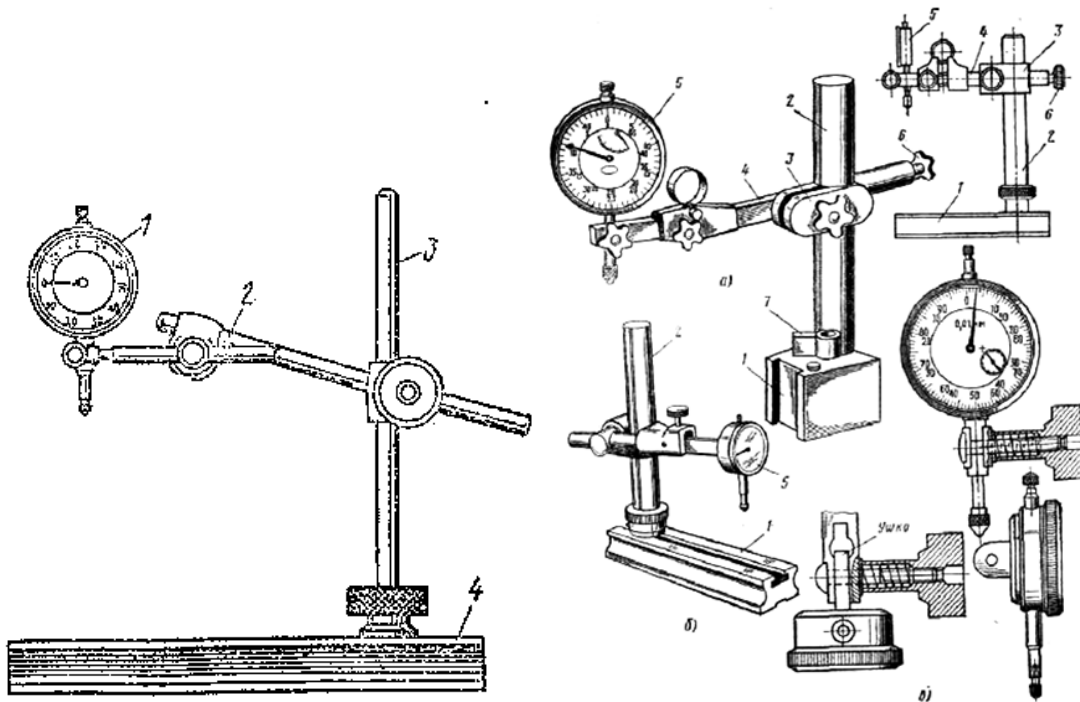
Стійки для закріплення індикатора годинникового типу
